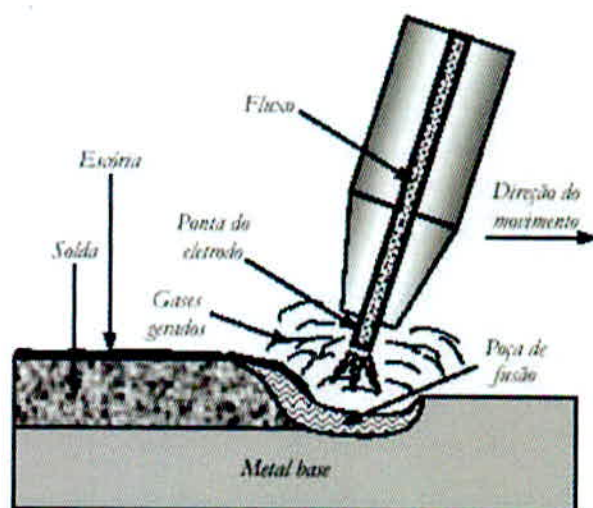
Representação do processo de soldagem a arco com eletrodo Tubular
